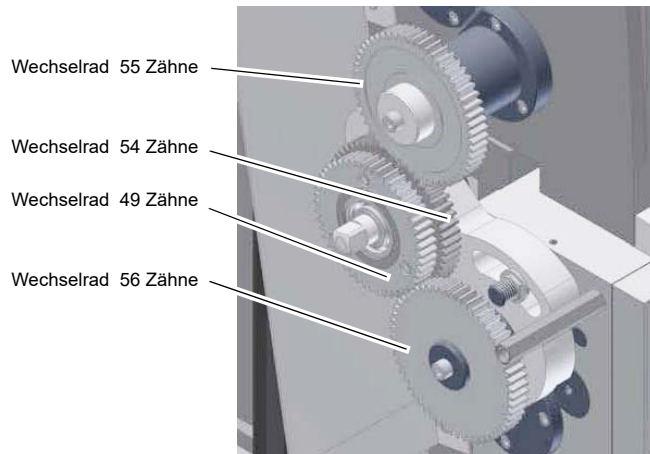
Wechselradposition für Metrische - und Zollgewinde
